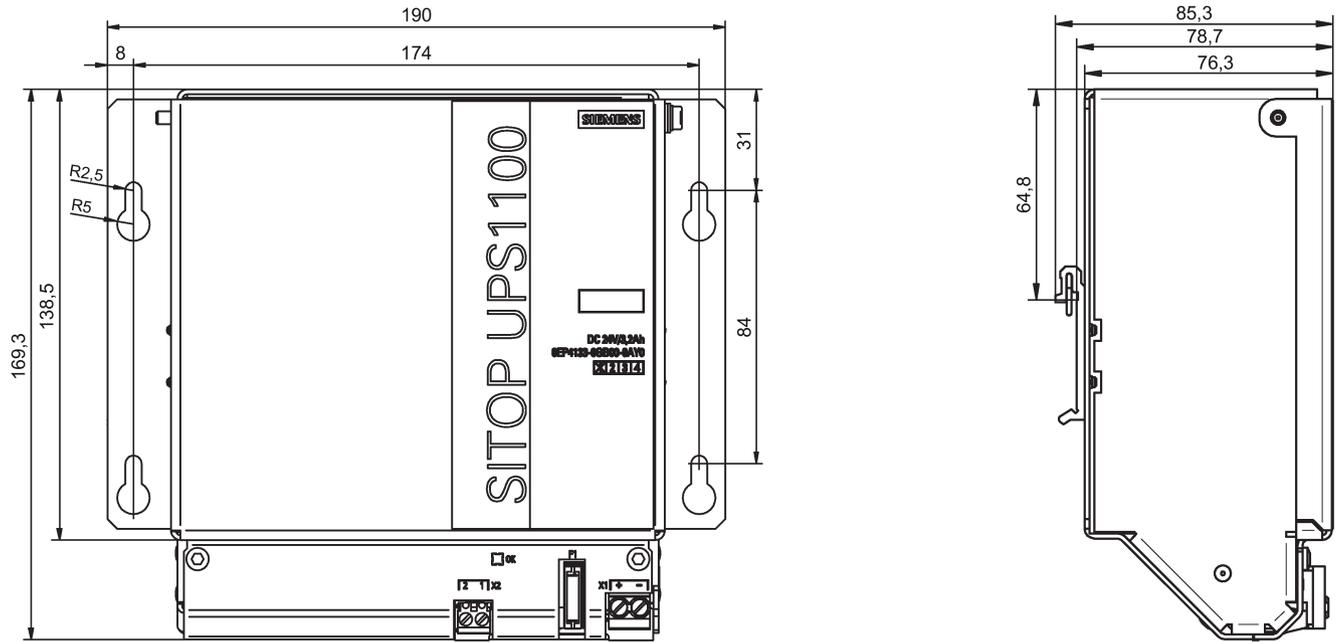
Maßzeichnung 6EP4133-0GB00-0AY0
